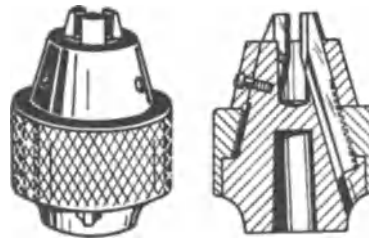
Dreibacken-Bohrfutter mit Spiraling (Flachgewinde).
